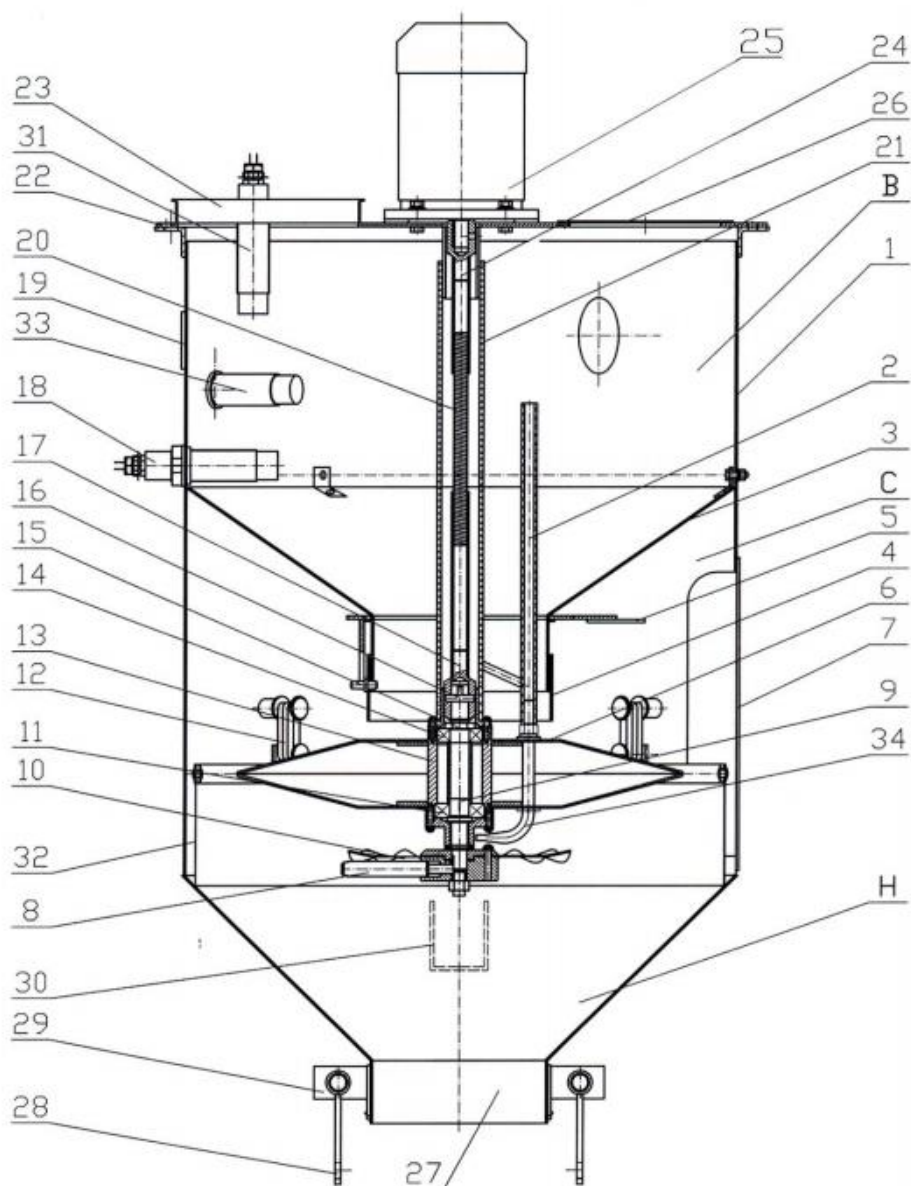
Схема модуля дозированного смешивания протравливателя семян ПСК-15: 1 – корпус; 2 – рукав; 3 – дозатор; 4 – заслонка дозатора; 5 – рычаг управления заслонкой; 6 – питатель; 7 – дверка; 8 – вибратор; 9 – вал питателя; 10 – распылитель; 11, 14 – подшипник; 12 – подвеска; 13 – корпус питателя; 15 – гайка подшипника; 16 – штифт распылителя; 17 – нижний наконечник; 18 – нижний датчик; 19 – верхний кронштейн крепления модуля; 20 – гибкий вал; 21 – кожух гибкого вала; 22 – крышка модуля; 23 – горловина; 24 – верхний наконечник; 25 – двигатель; 26 – люк; 27 – горловина выходная; 28 – звено для установки шнека; 29 – поворотный держатель; 30 – нижний кронштейн крепления модуля; 31 – верхний датчик; 32 – фартук питателя; 33 – средний датчик; 34 – трубка; В – верхняя камера; С – средняя камера; Н – нижняя камера
